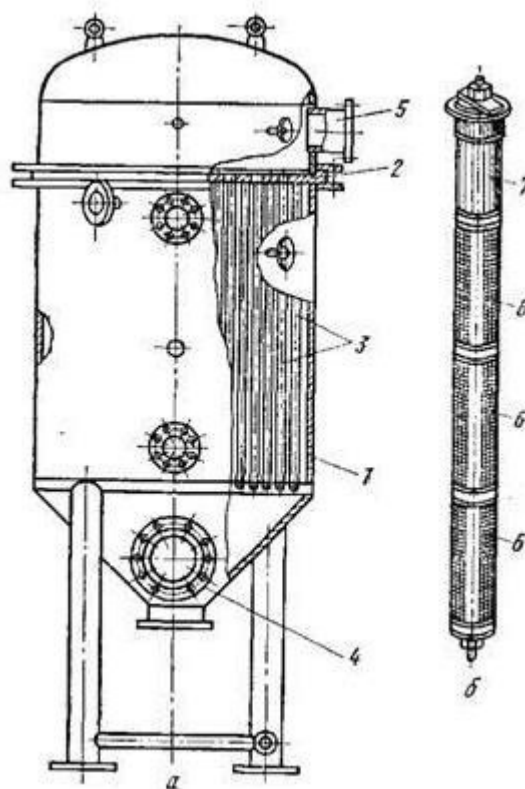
Патронний фільтр: а - загальний вигляд; б - патрон.
